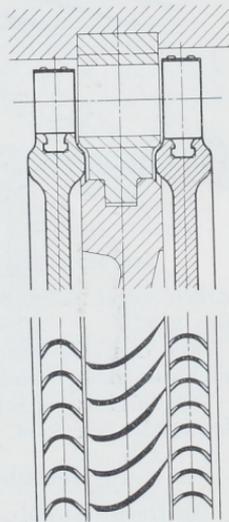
Turbine mit Blechschaufeln und Zwischenböden mit besonderen Kränzen.
